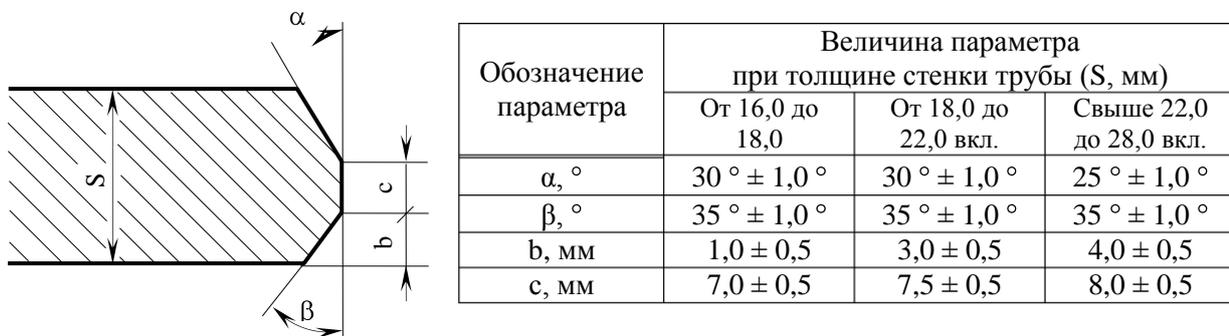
Геометрические параметры разделки кромок труб для двухсторонней автоматической сварки под флюсом
